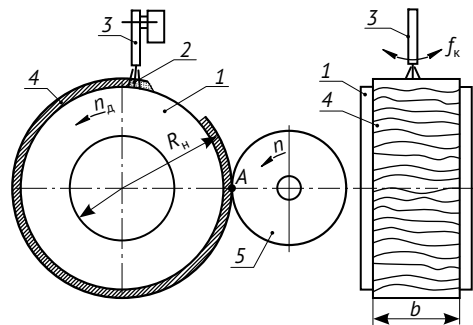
Расчетная схема широкоослойной наплавки колеблющимся электродом и механической обработки металлопокрытия детали
